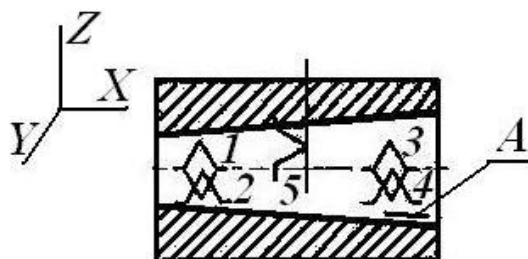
Базування деталі по довгій конічній поверхні
